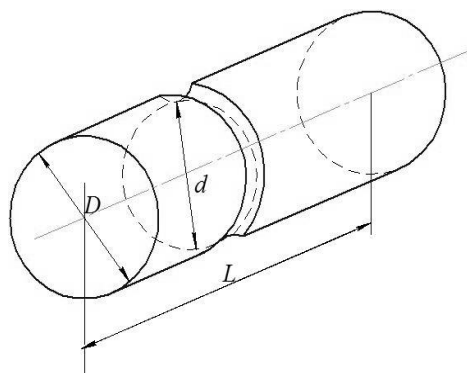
Цилиндрическая деталь с круговым надрезом полукруглого профиля
